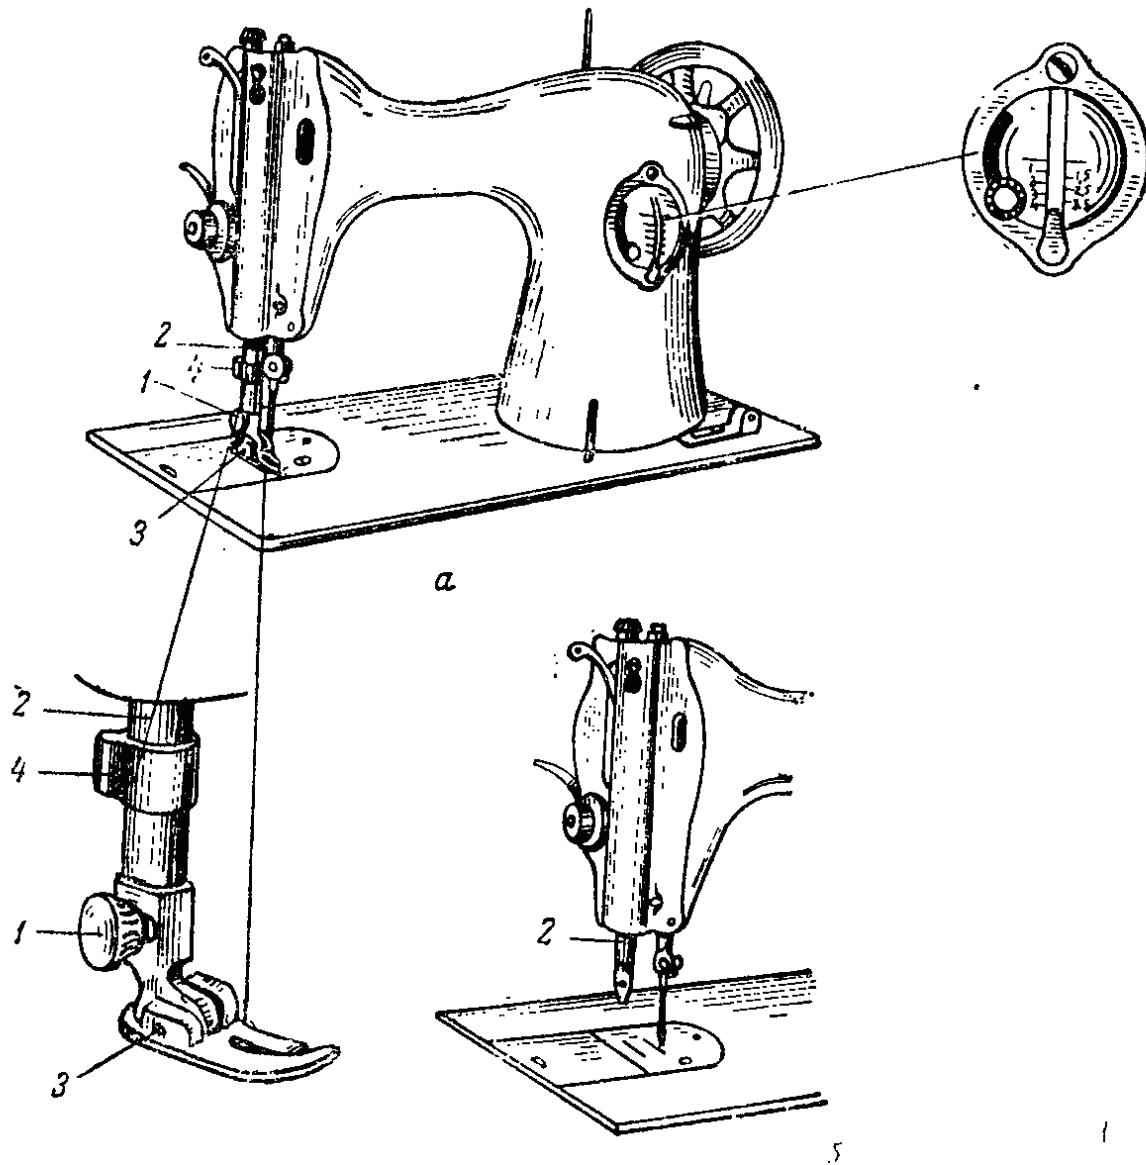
Подготовка машины к креплению приставки „зигзаг“:
